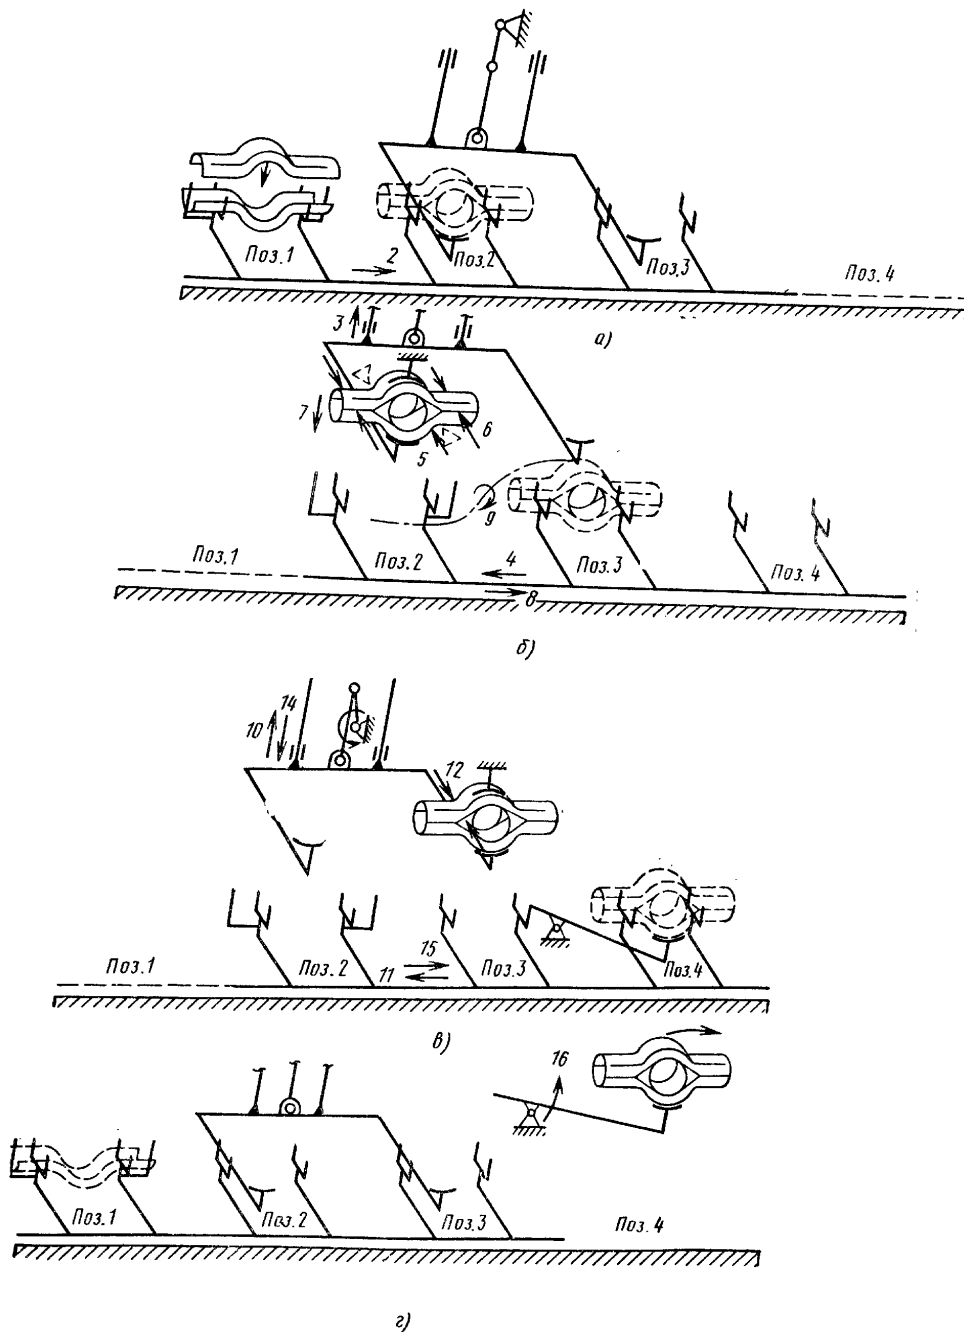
Схема выполнения сборочно-сварочных операций на стенде 1
